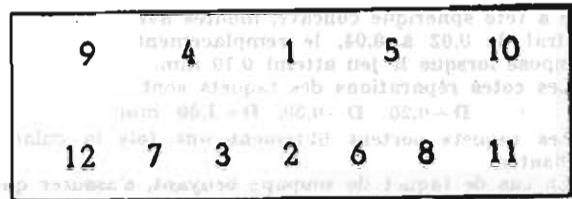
Ordre de serrage des écrous ou vis de culasse
